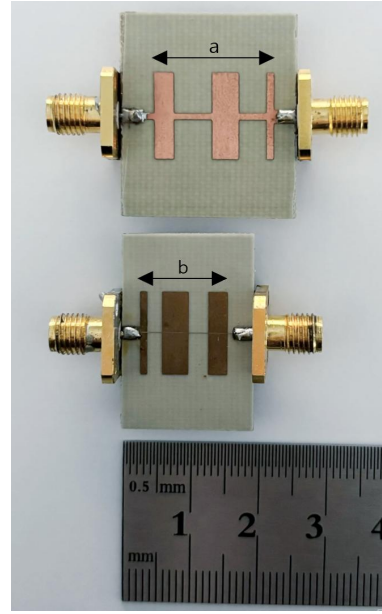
PCB 에칭 공정과 AJP 프린팅 공정에 의한 계단형 임피던스 저역 통과 여파기 사진
